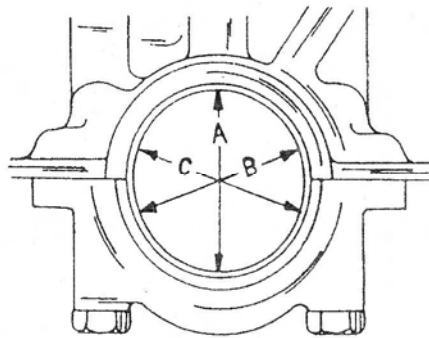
Измерение основного отверстия подшипника коленчатого вала.
